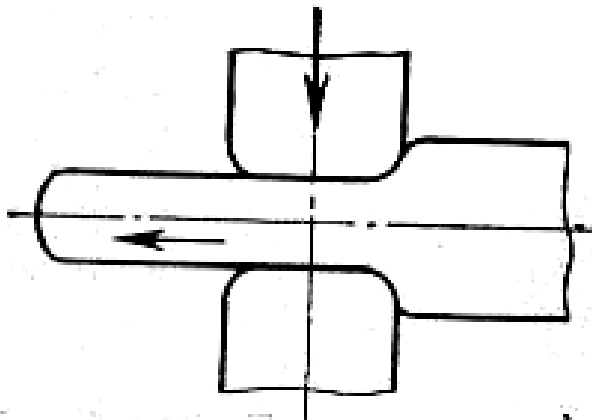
Схема выполнения плоской протяжки заготовки
